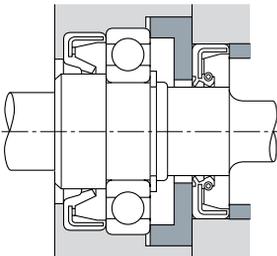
Exemple de Montage d'un Joint à Lèvre (1)
